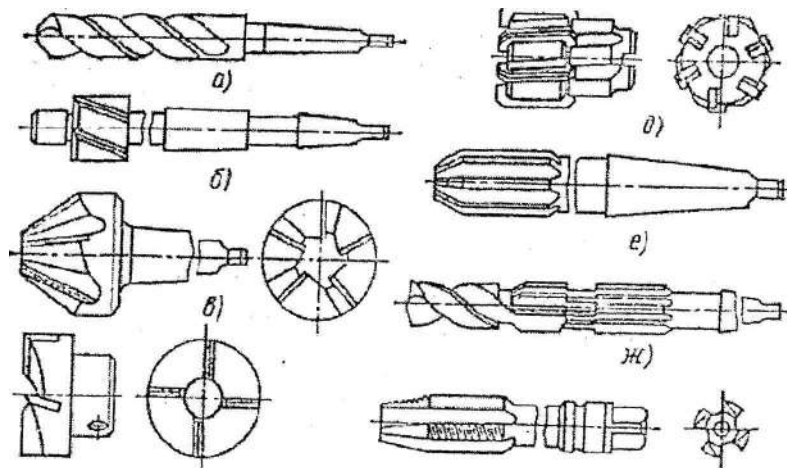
Режущие инструменты, применяемые на сверлильных станках
